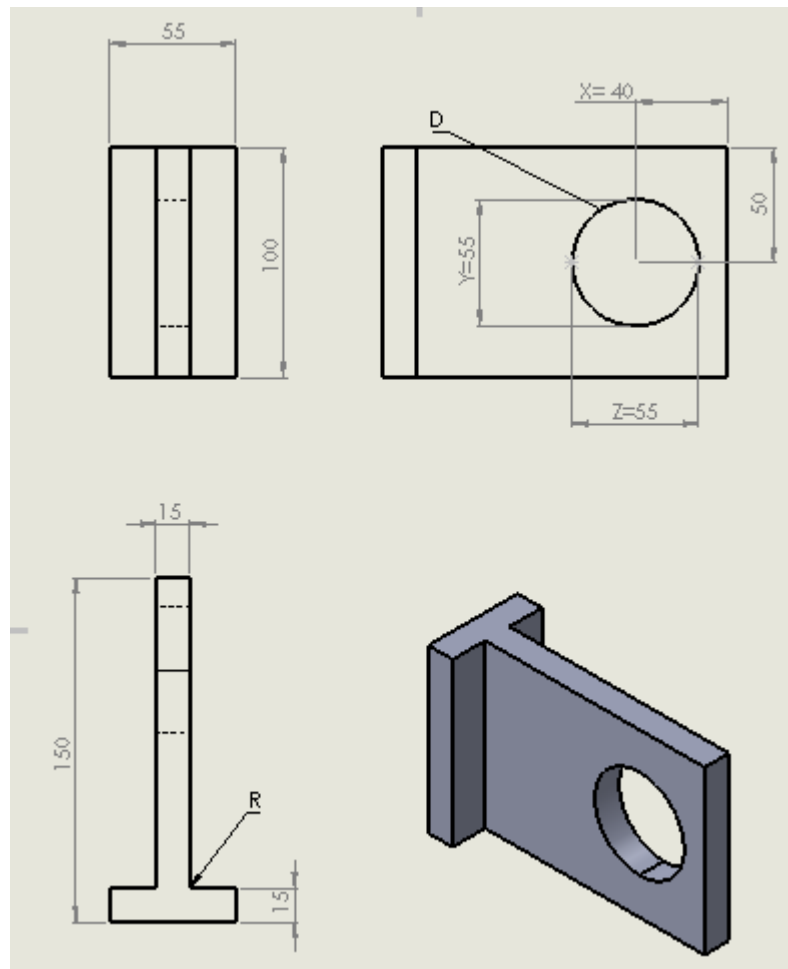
PLANO DE PIEZA MECANICA ACOTADO
